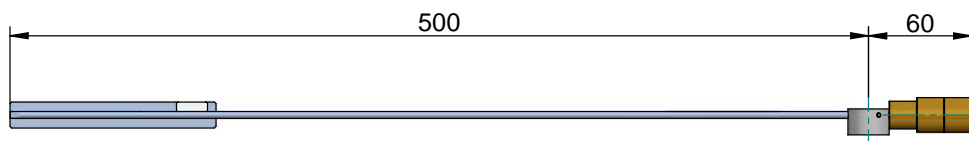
Abmessungen in mm mit 3 Gegengewichten
